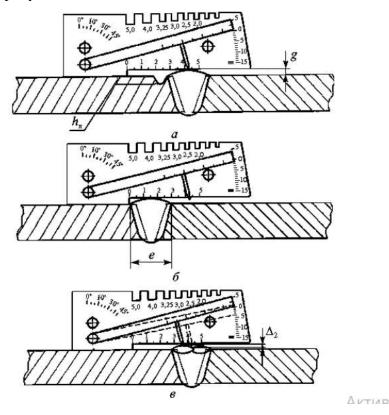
Измерения с помощью шаблона УШС размеров сварного шва а - измерение высоты шва (g) и глубины подреза (h $_{\rm II}$); б - измерение ширины шва (e); в - измерение западаний между валиками (Δ_2)
